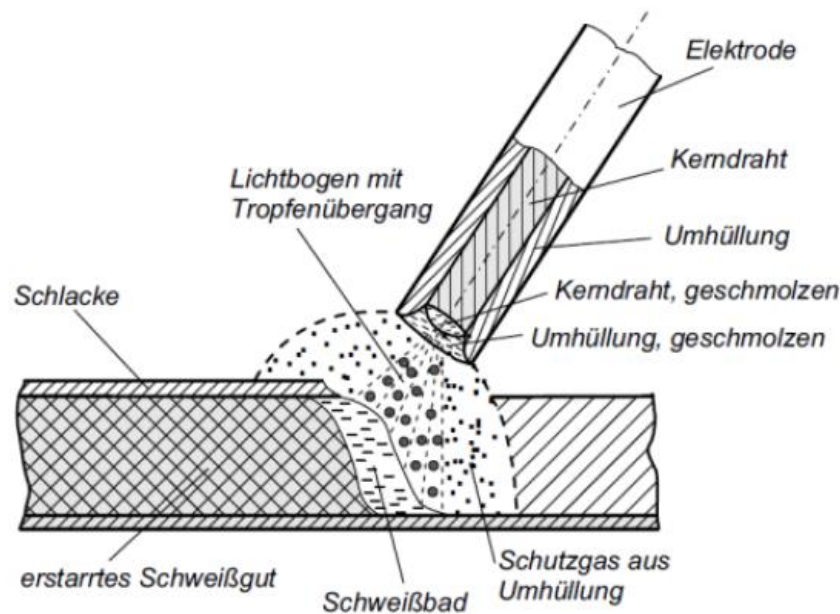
Schutzgasschweißen. Die charakteristischen Komponenten und Begriffe in einem Schutzgasschweißverfahren [3].
